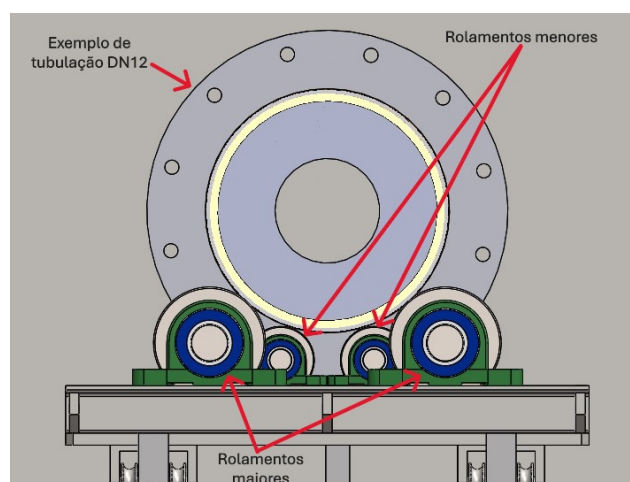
Tubulação DN12 apoiada nos rolamentos maiores.
